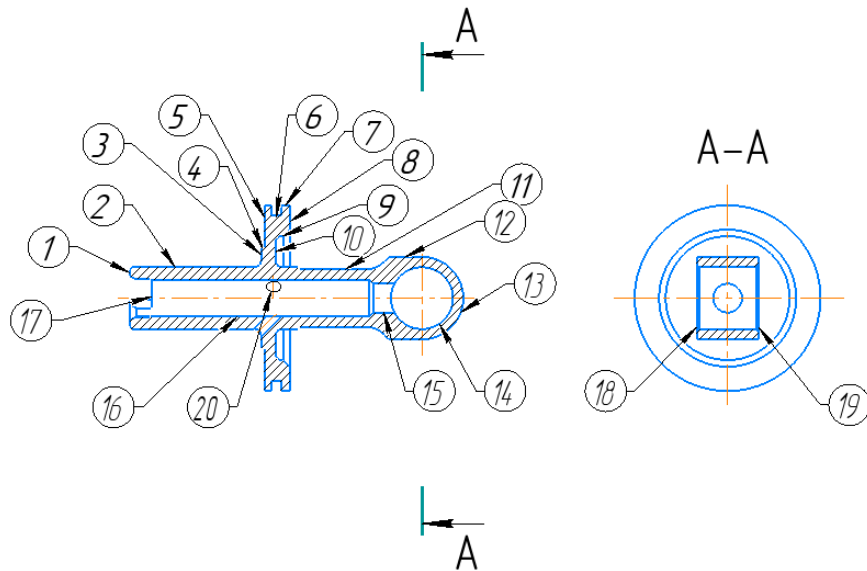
Ескіз деталі з позначенням поверхонь
